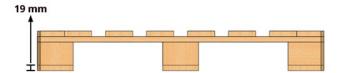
Esquema de vista lateral de um pallet com tábuas inferiores de 19 mm de espessura.
